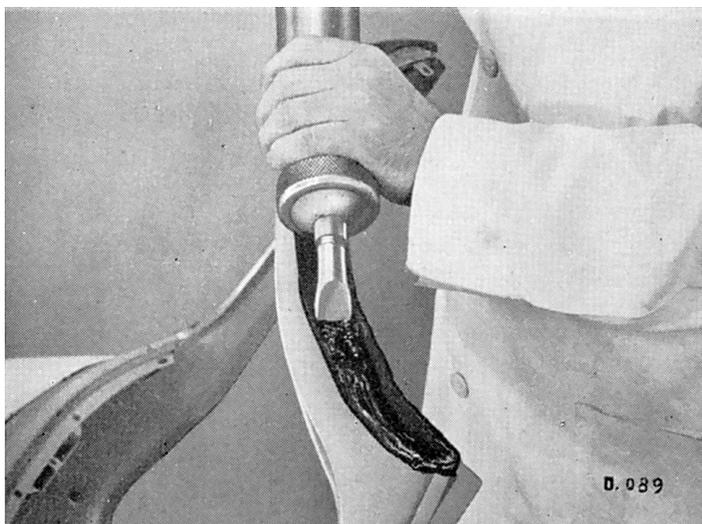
Application de produit d'étanchéité sur le joint du cadre de pare-brise
